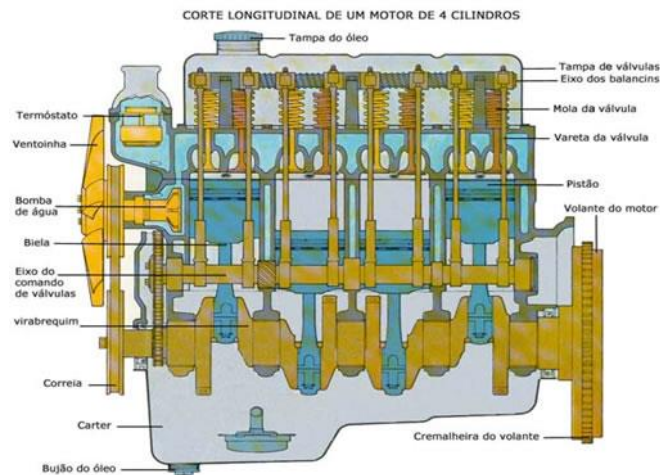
Imagem em corte longitudinal de um motor de combustão interna [A3].
